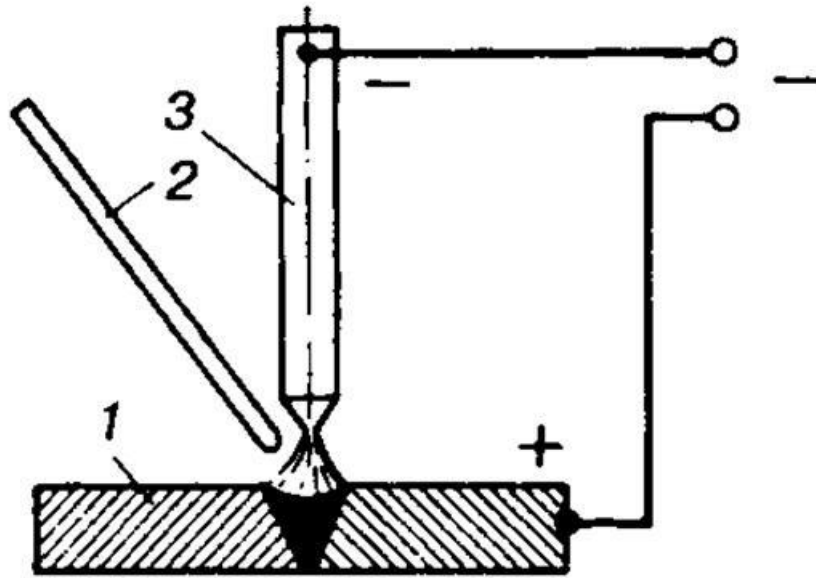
Схема дугового зварювання неплавким вугільним електродом
